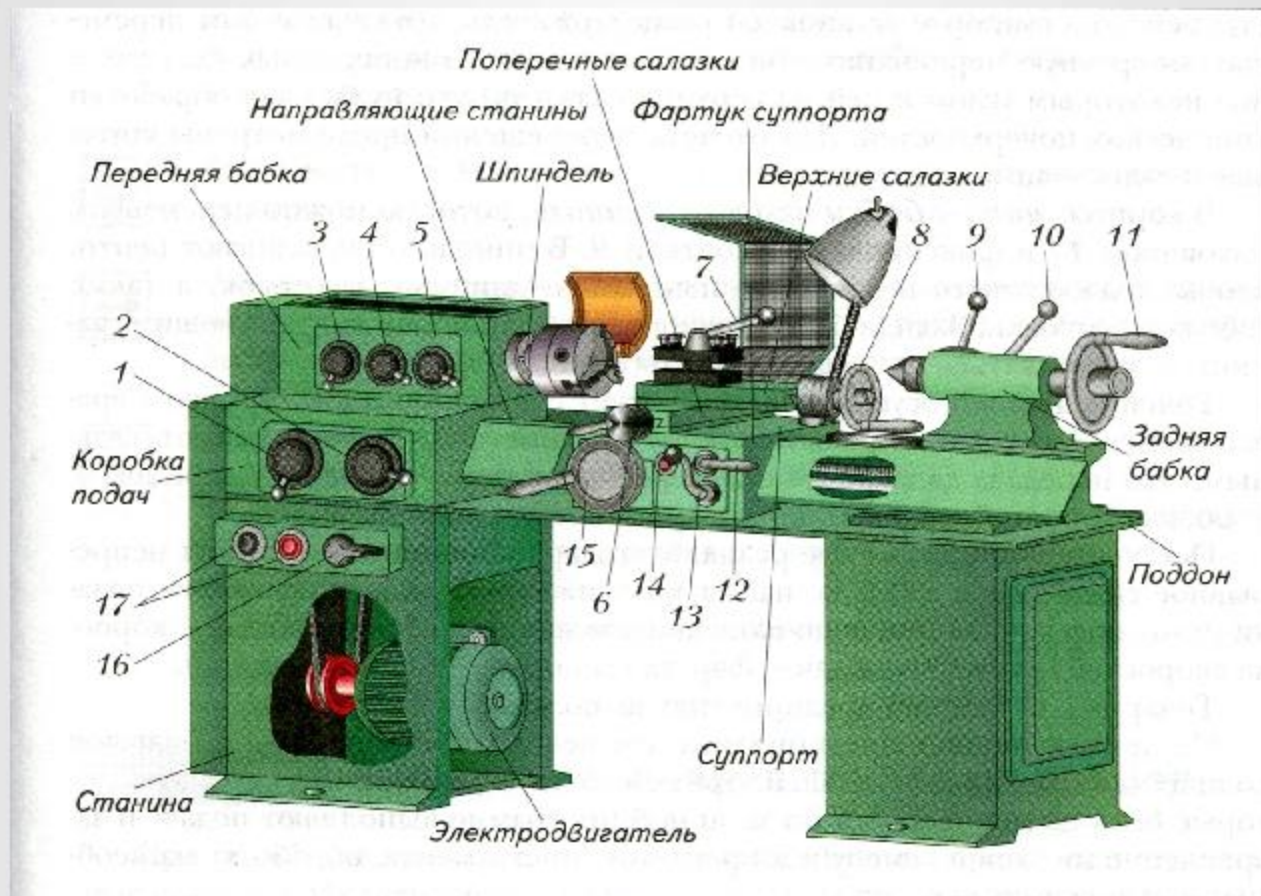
Токарно-винторезный станок ТВ-6: 1, 2 – рукоятки переключения величины подачи; 3 – рукоятка переключения гитарного механизма; 4, 5 – рукоятки переключения частоты вращения шпинделя; 6 – рукоятка поперечной подачи суппорта; 7 – рукоятка закрепления резцедержателя; 8 – рукоятка перемещения верхних салазок; 9 – рукоятка крепления пиноли; 10 – рукоятка крепления задней бабки; 11 – маховик подачи пиноли; 12, 13 – рукоятки управления механической подачей; 14 – кнопка включения ременной передачи; 15 – маховик перемещения суппорта; 16 – рукоятка реверса; 17 – кнопки включения и отключения электродвигателя
